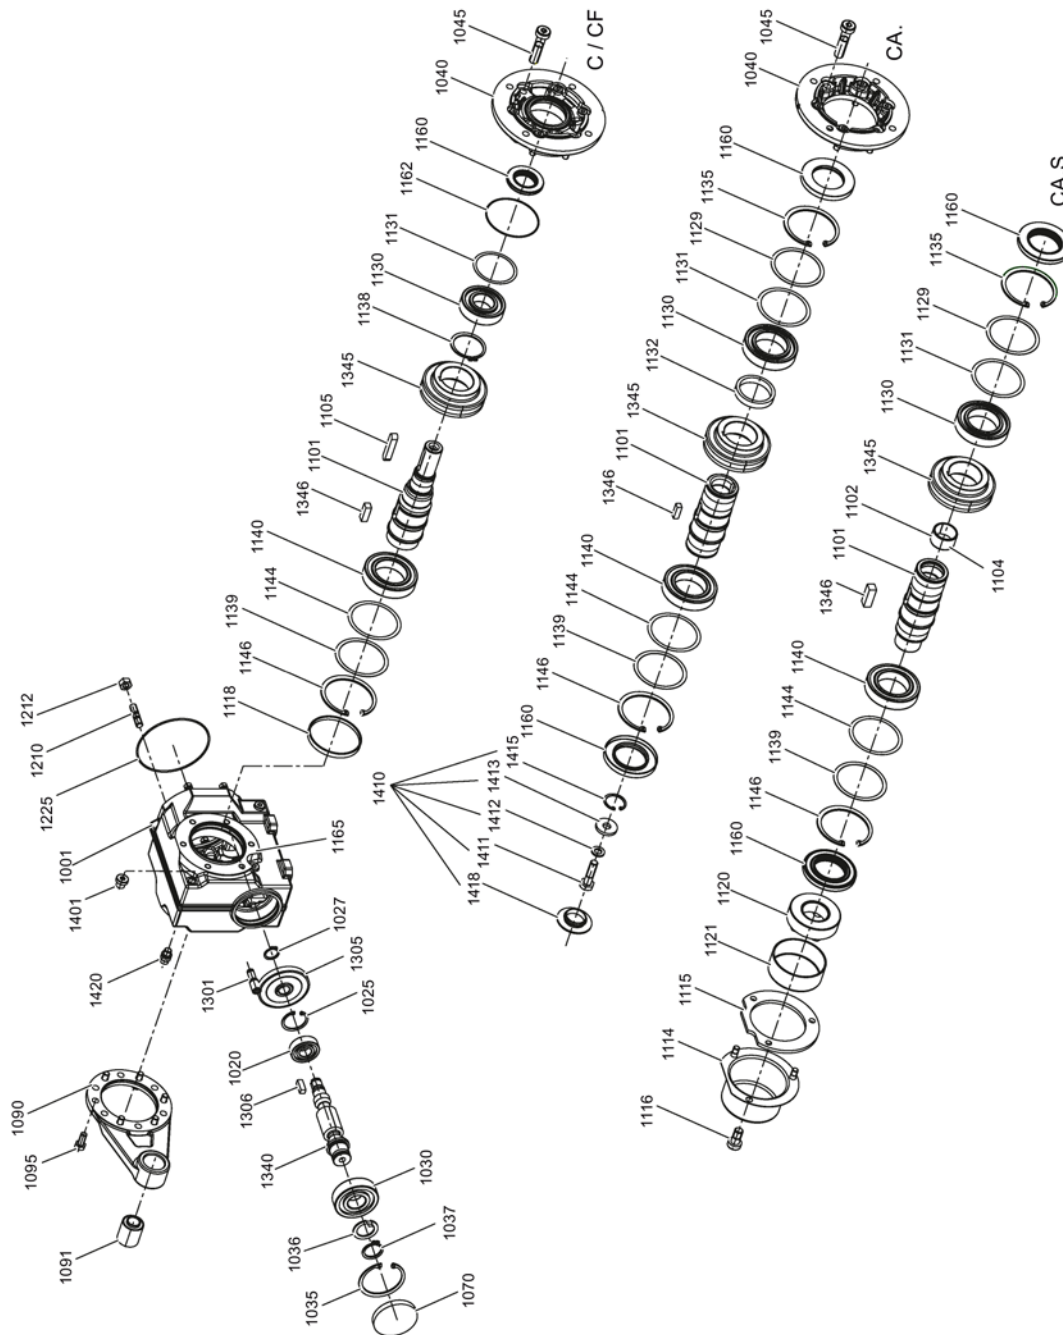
Конический редуктор К типоразмеров 39-189
